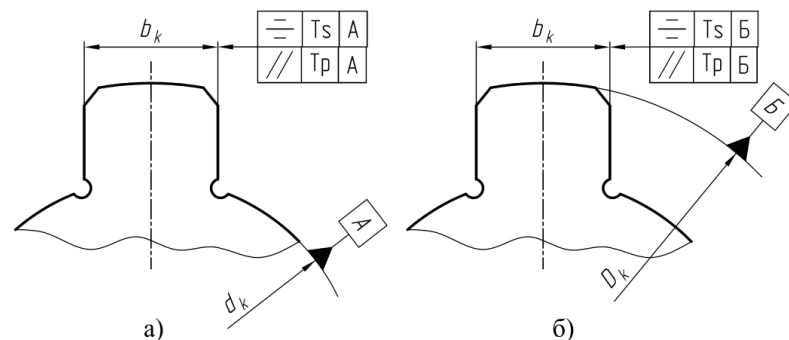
Схема позначення допуску симетричності Ts та паралельності Tr зуба калібра-пробки на кресленику ; а) – центрування за d ; б) - центрування за D або b [22].
